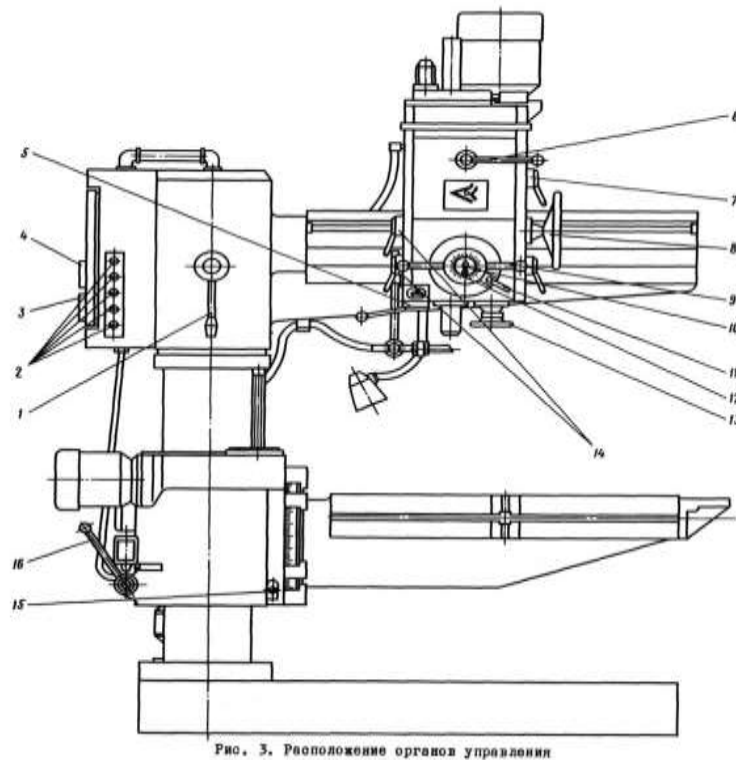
Свердильний верстат 2Л53У[4]
